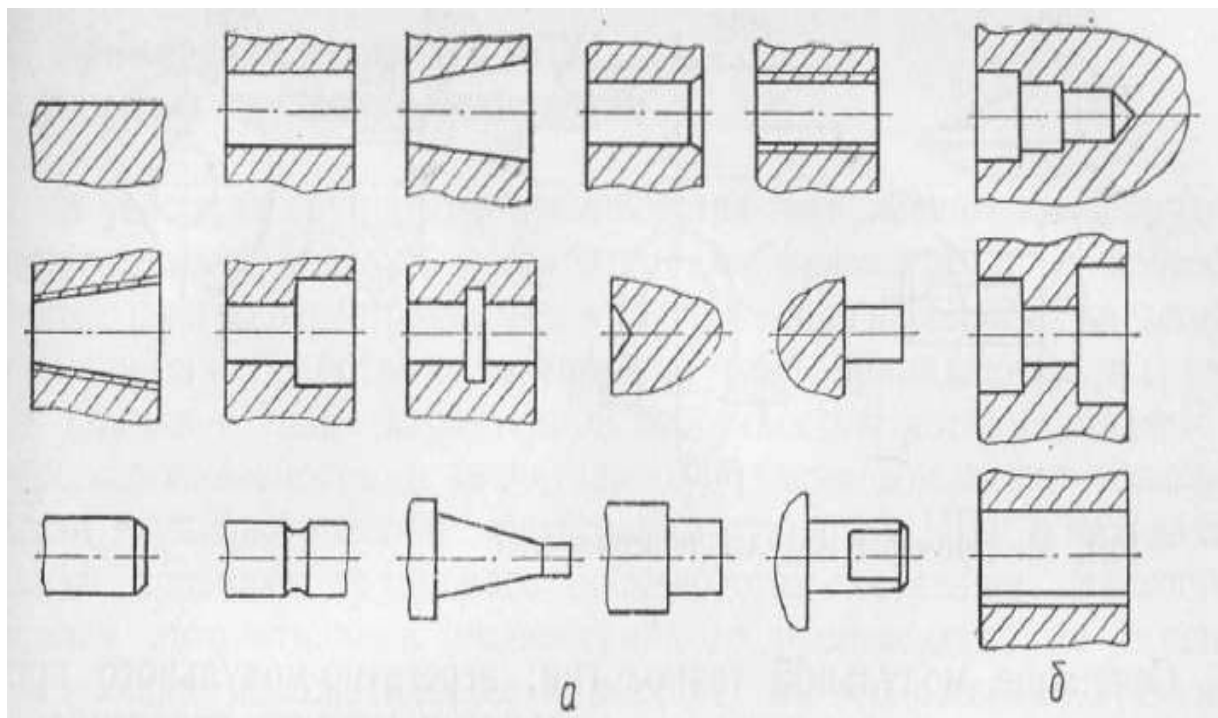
Типові елементи форми (а) і комплекси (б) корпусних деталей
